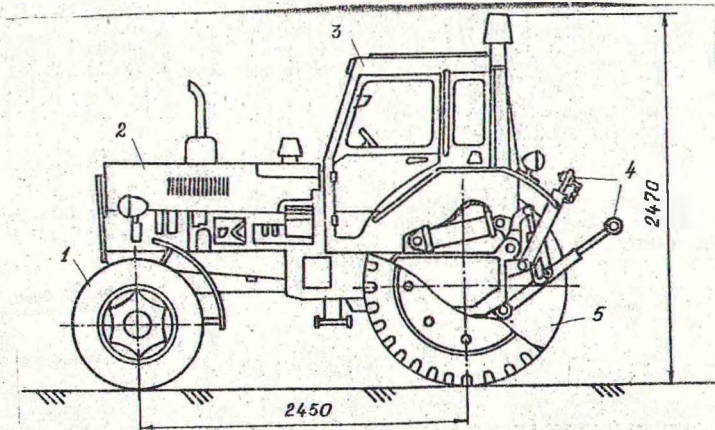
Колесный трактор МТЗ-82: 1-передний ведущий
